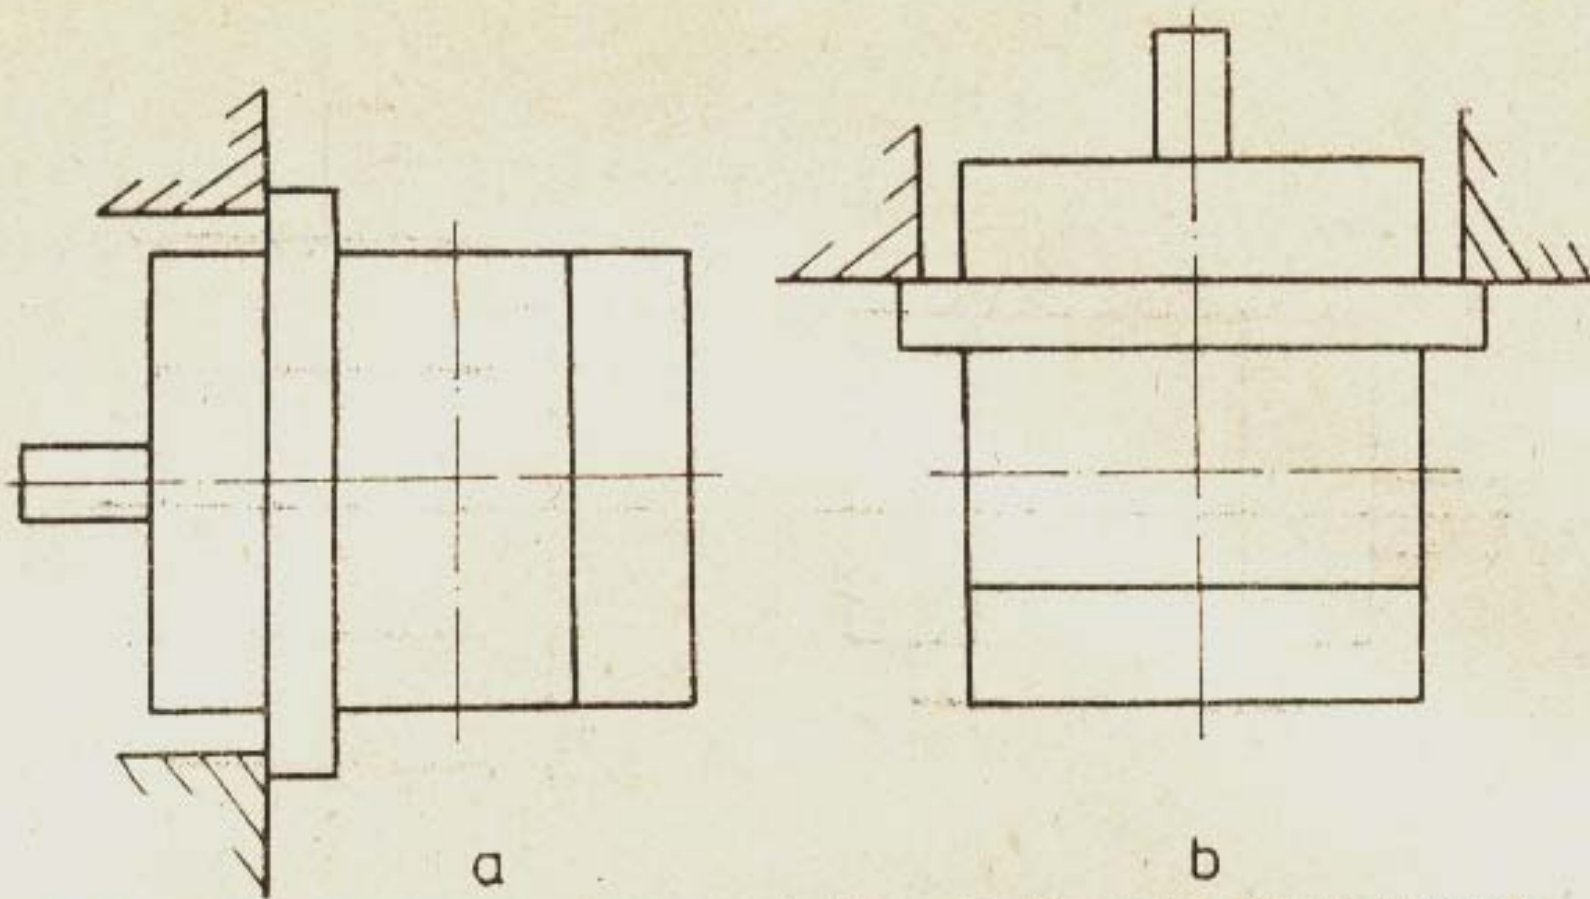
Maşini fără tălpi, cu scuturi portlagăr şi flanşă pe carcasă :
